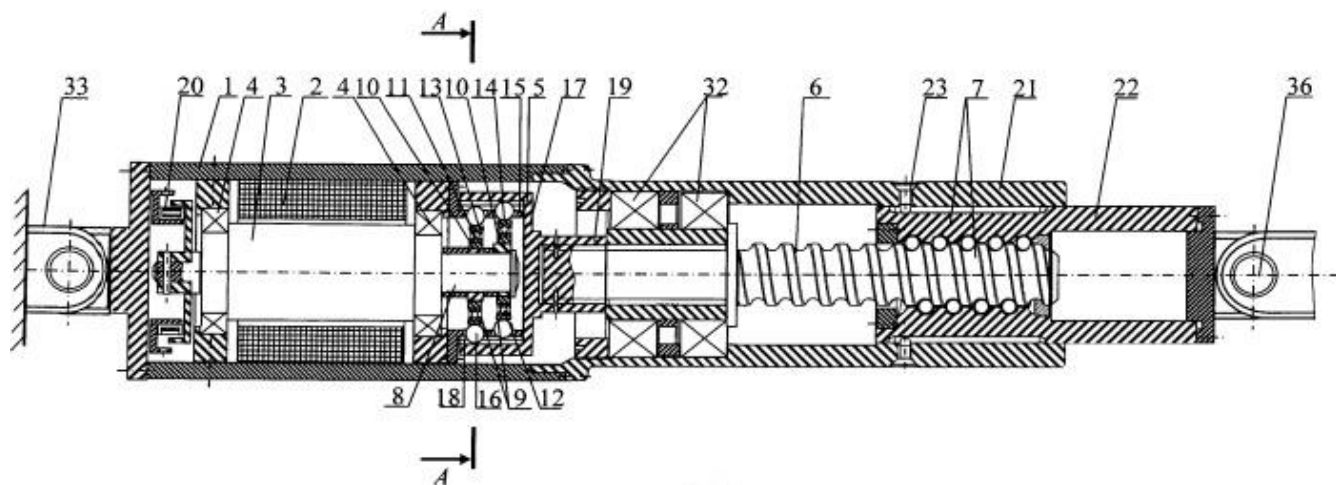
Схема приводу: 1 – корпус; 2 – електродвигун; 3 – ротор; 4 – підшипники; 5 – хвильовий редуктор; 6 – гвинт; 7 – шарико-гвинтовий механізм; 8 – вал ротора; 9 – хвильоутворювач; 10 – ексцентрики; 11, 12 – підшипники; 13, 14 – робочі кільця; 15 – сепаратор; 16 – тіла обертання; 17 – жорстке колесо; 18 – хвильова поверхня; 19 – вал; 20 – датчик положення вала; 21 – корпус; 22 – штовхач; 23 – стопор.
